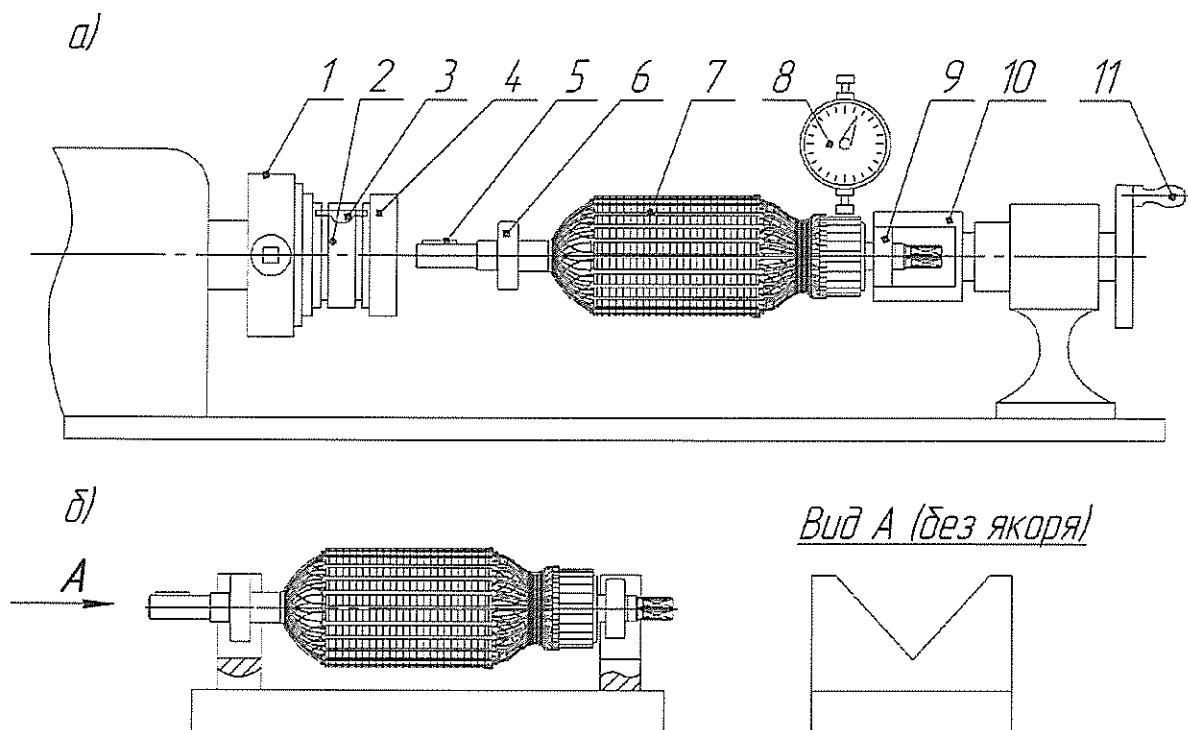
Приспособление для обработки коллектора (а) и проверки биения коллектора (б)
